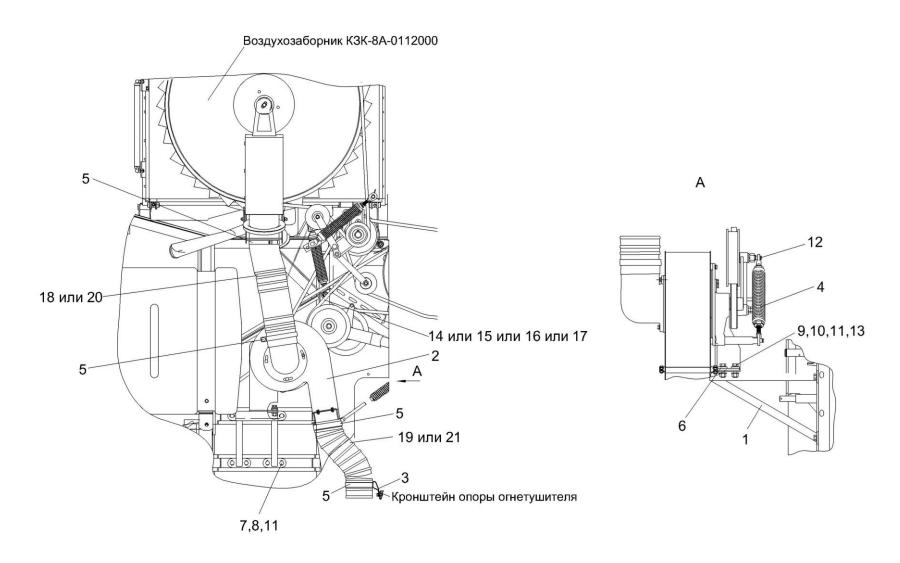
Установка вентилятора КЗК-8А-0112100
